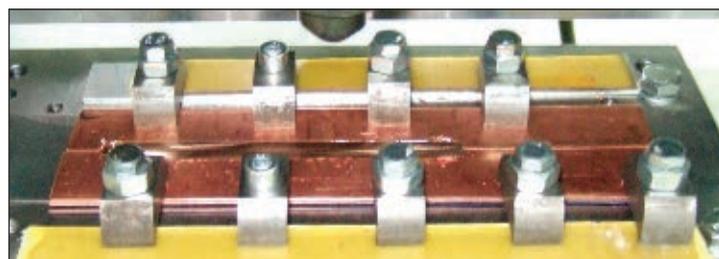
Медные пластины после сварки трением с перемешиванием
